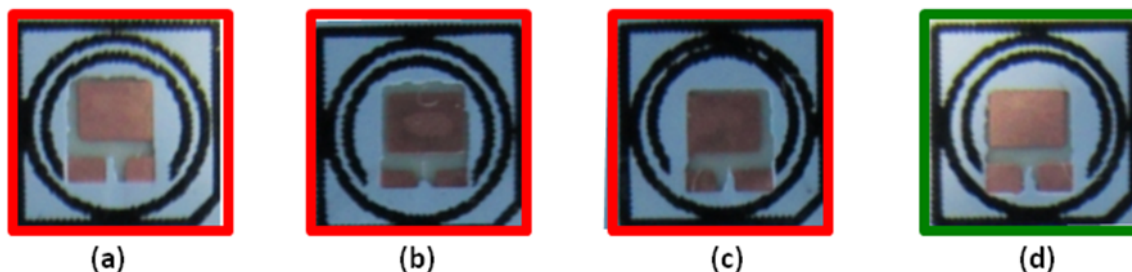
在制造PCB板期间，倘若有关顶部金属阻焊层的定位控制不准的话，就会影响PCB板上实际的焊盘尺寸。案例中的四张图片都取材于同一物理四层PCB板。PCB板(a)处至(c)处的阴极与阳极的实际尺寸比原先设计的要小。仅有(d)处的焊盘尺寸仍在规范当中。
